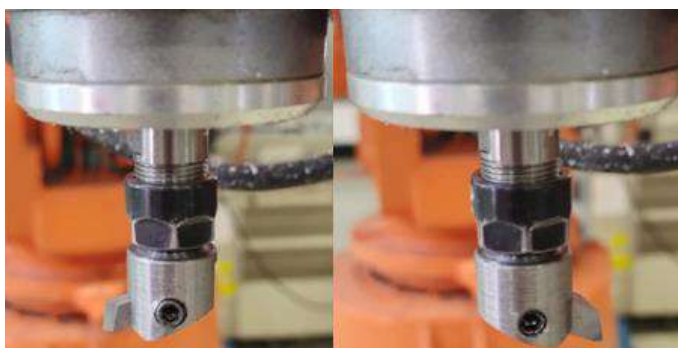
Herramienta de corte de diámetro 30 mm.
